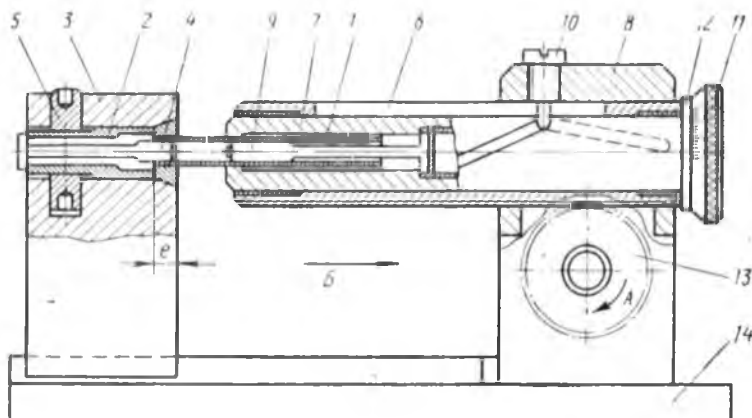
Приспособление для скручивания волноводов миллиметрового диапазона с применением жесткой калибрующей оправки
